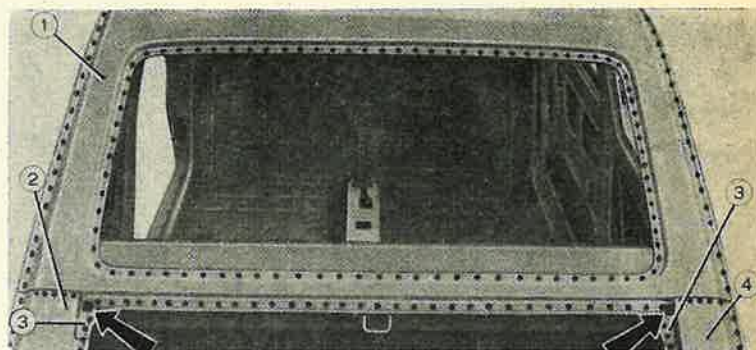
Liaisons par points de soudure des pièces composant la baie de lunette arrière.
